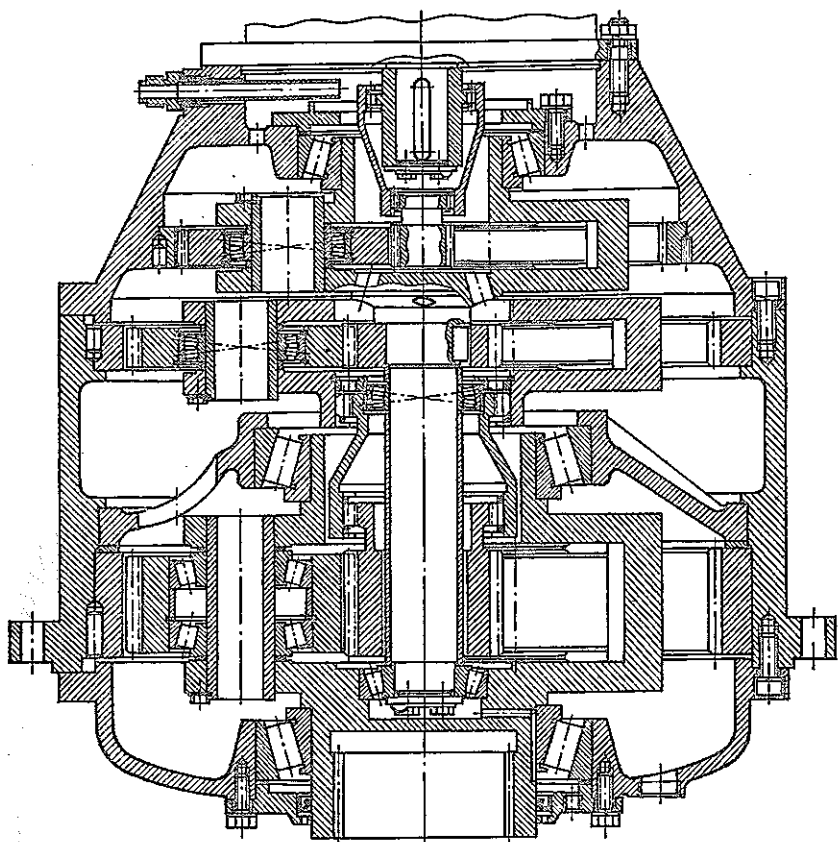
Трехступенчатый вертикальный мотор-редуктор
